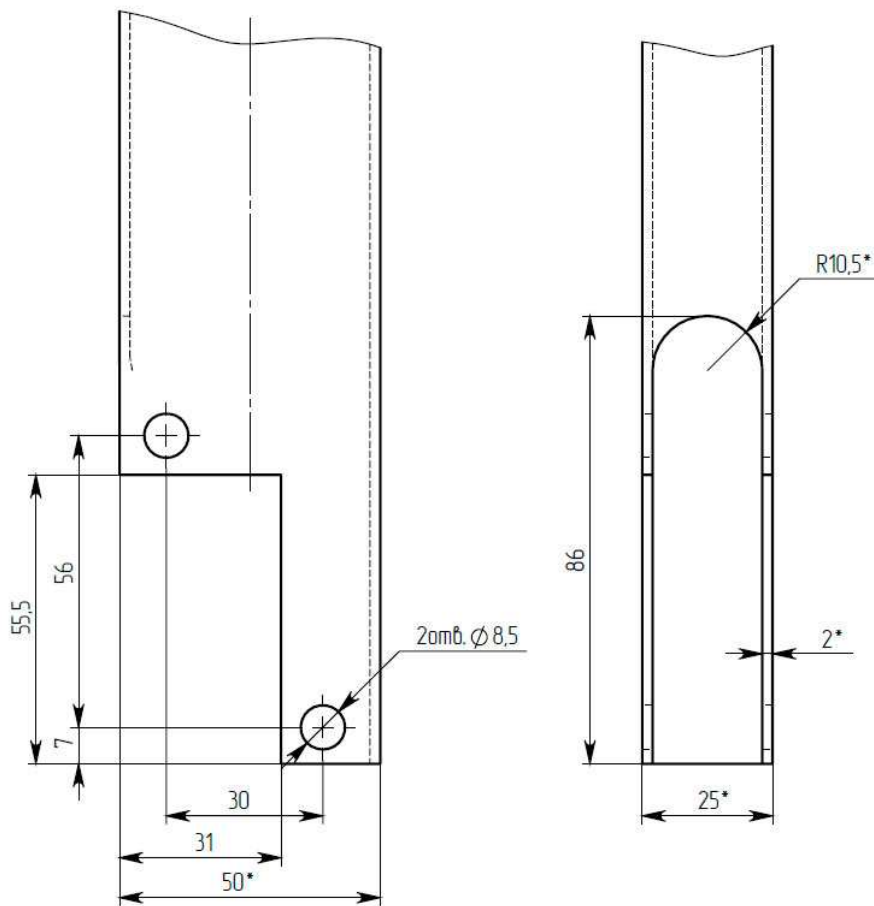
Разметка штанги 50x25 мм для крепления моноблока
